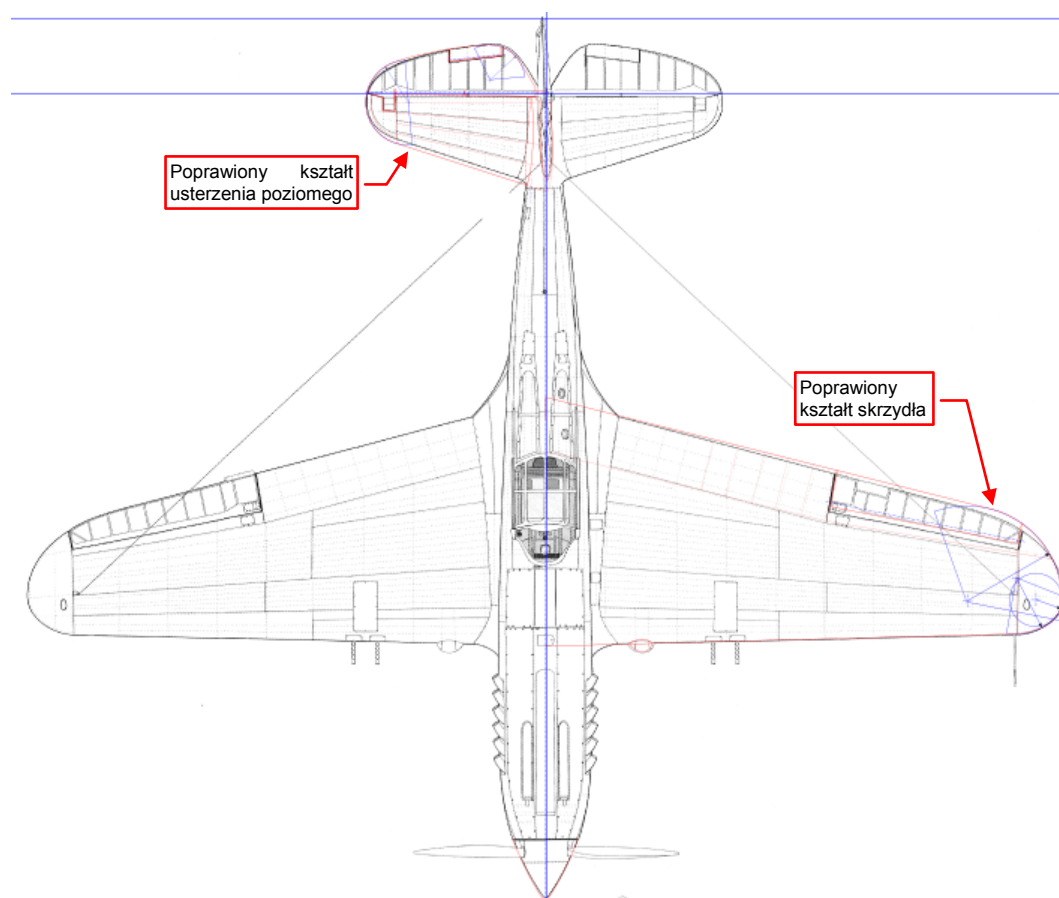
przedstawia korekty naniesione na plan usterzenia poziomego (statecznika i steru).
